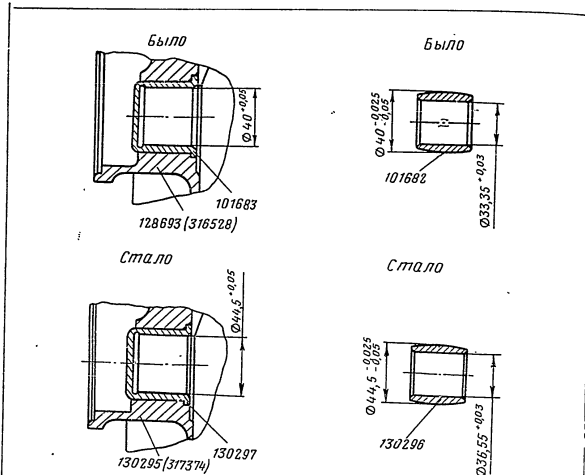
Сателлит валика редуктора двухскоростной передачи нагнетателя (собранный).
